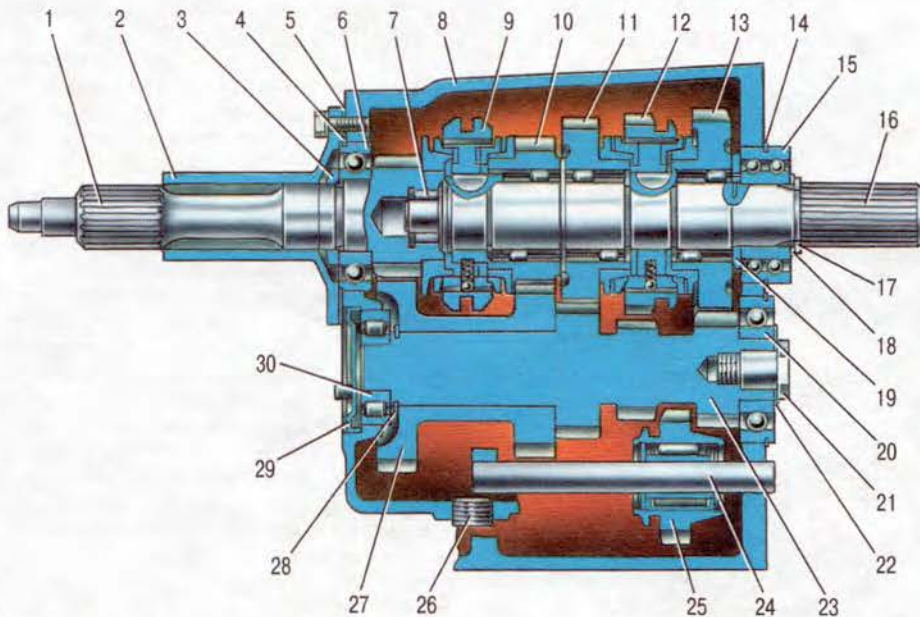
Принципиальная схема коробки передач: 1 – первичный вал; 2 – передняя крышка первичного вала; 3 – специальная гайка; 4, 14, 17, 28 – стопорные кольца; 5 – прокладка; 6, 15, 20, 30 – подшипники; 7 – передний подшипник ведомого вала; 8 – картер; 9 – муфта синхронизатора III и IV передач; 10 – шестерня III передачи; 11 – шестерня II передачи; 12 – муфта синхронизатора I и II передач; 13 – шестерня I передачи; 16 – вторичный вал; 18 – шайба; 19 – распорное кольцо; 21 – специальный болт; 22 – тарельчатая пружина; 23 – промежуточный вал; 24 – ось шестерни заднего хода; 25 – шестерня передачи заднего хода; 26 – пробка отверстия для слива масла; 27 – блок шестерен привода промежуточного вала и III передачи; 29 – крышка
